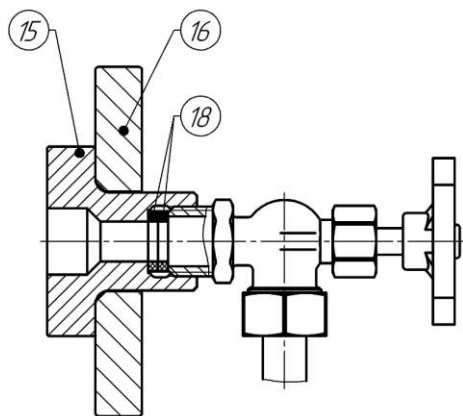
Общий вид указателя с присоединительным фланцем Ду20 и резьбовым соединителем (остальное – см. рисунок 7.1.1)
